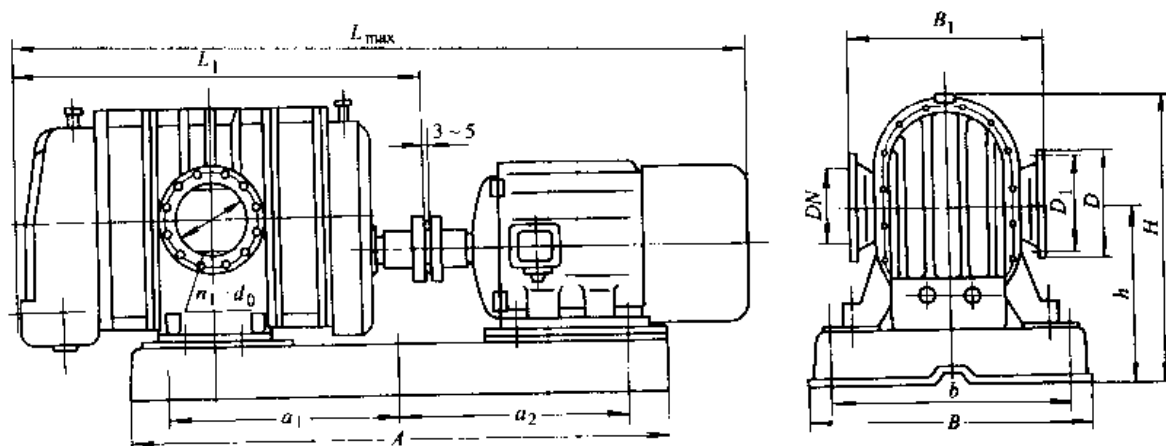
L51LD、…、L54LD 罗茨鼓风机外形尺寸图
